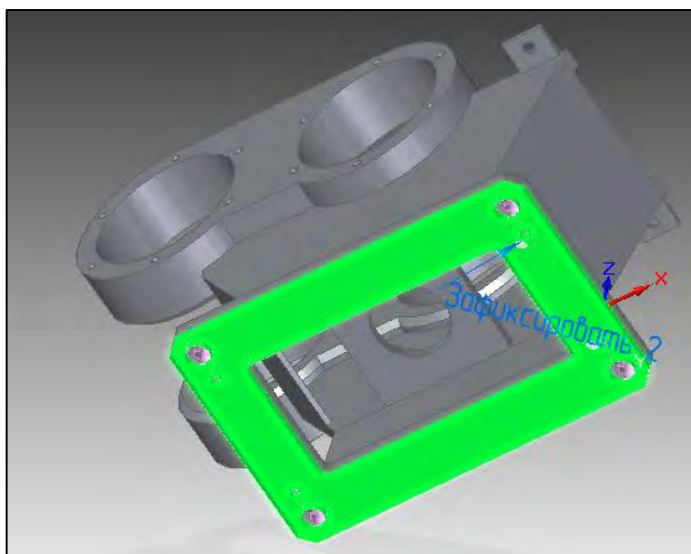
Установка закрепления нижней части корпуса ВУ в пространстве
